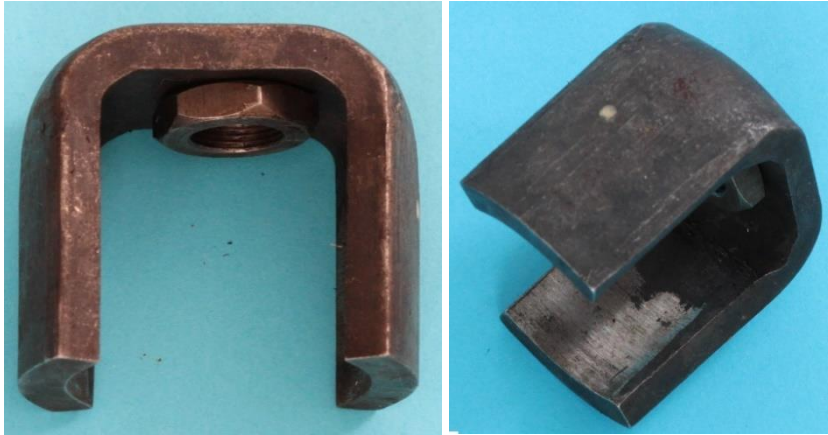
Zwei Ansichten des Tulpenmagneten
